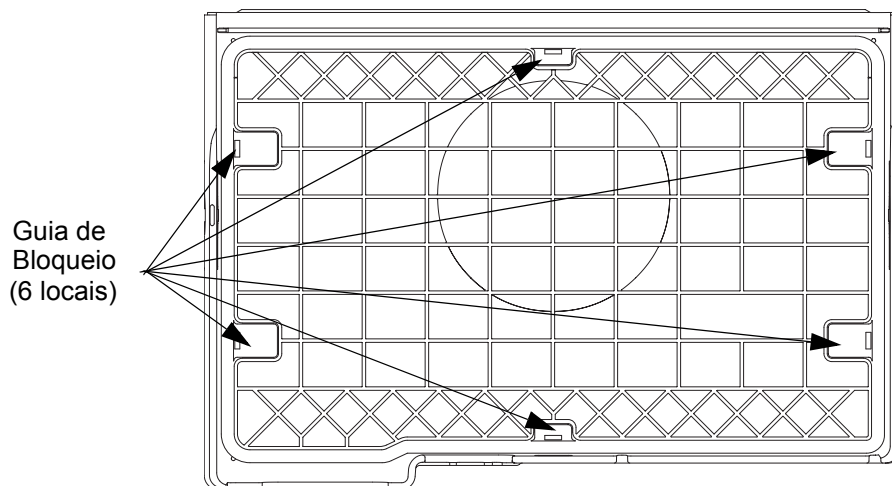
Inspeção de Montagem da Tampa com Vedação
